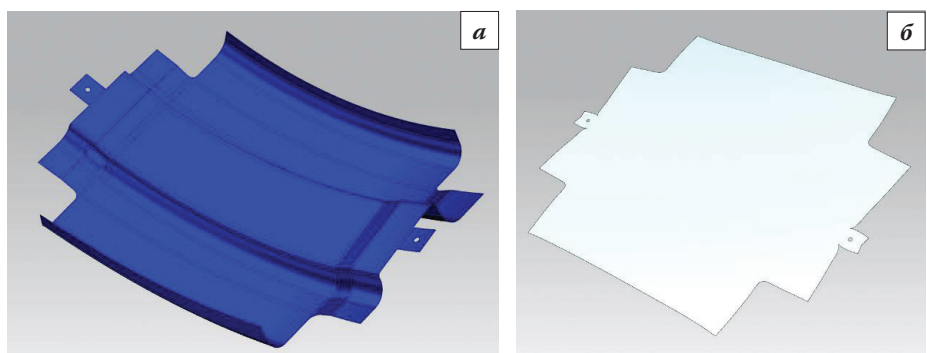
Развертка, полученная в PAM-STAMP 2G: а – деталь с приливами под шпильчные отверстия; б – физическая развертка с учетом параметров материала
